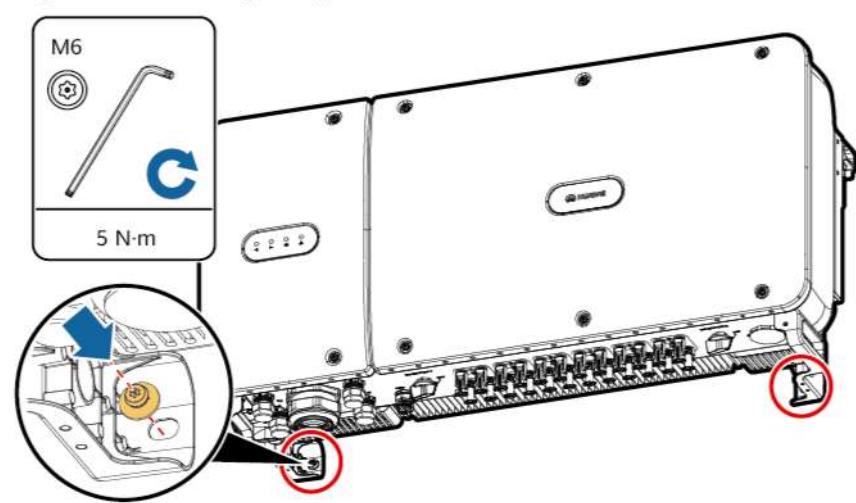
Montagem do SUN2000 em um suporte de montagem
